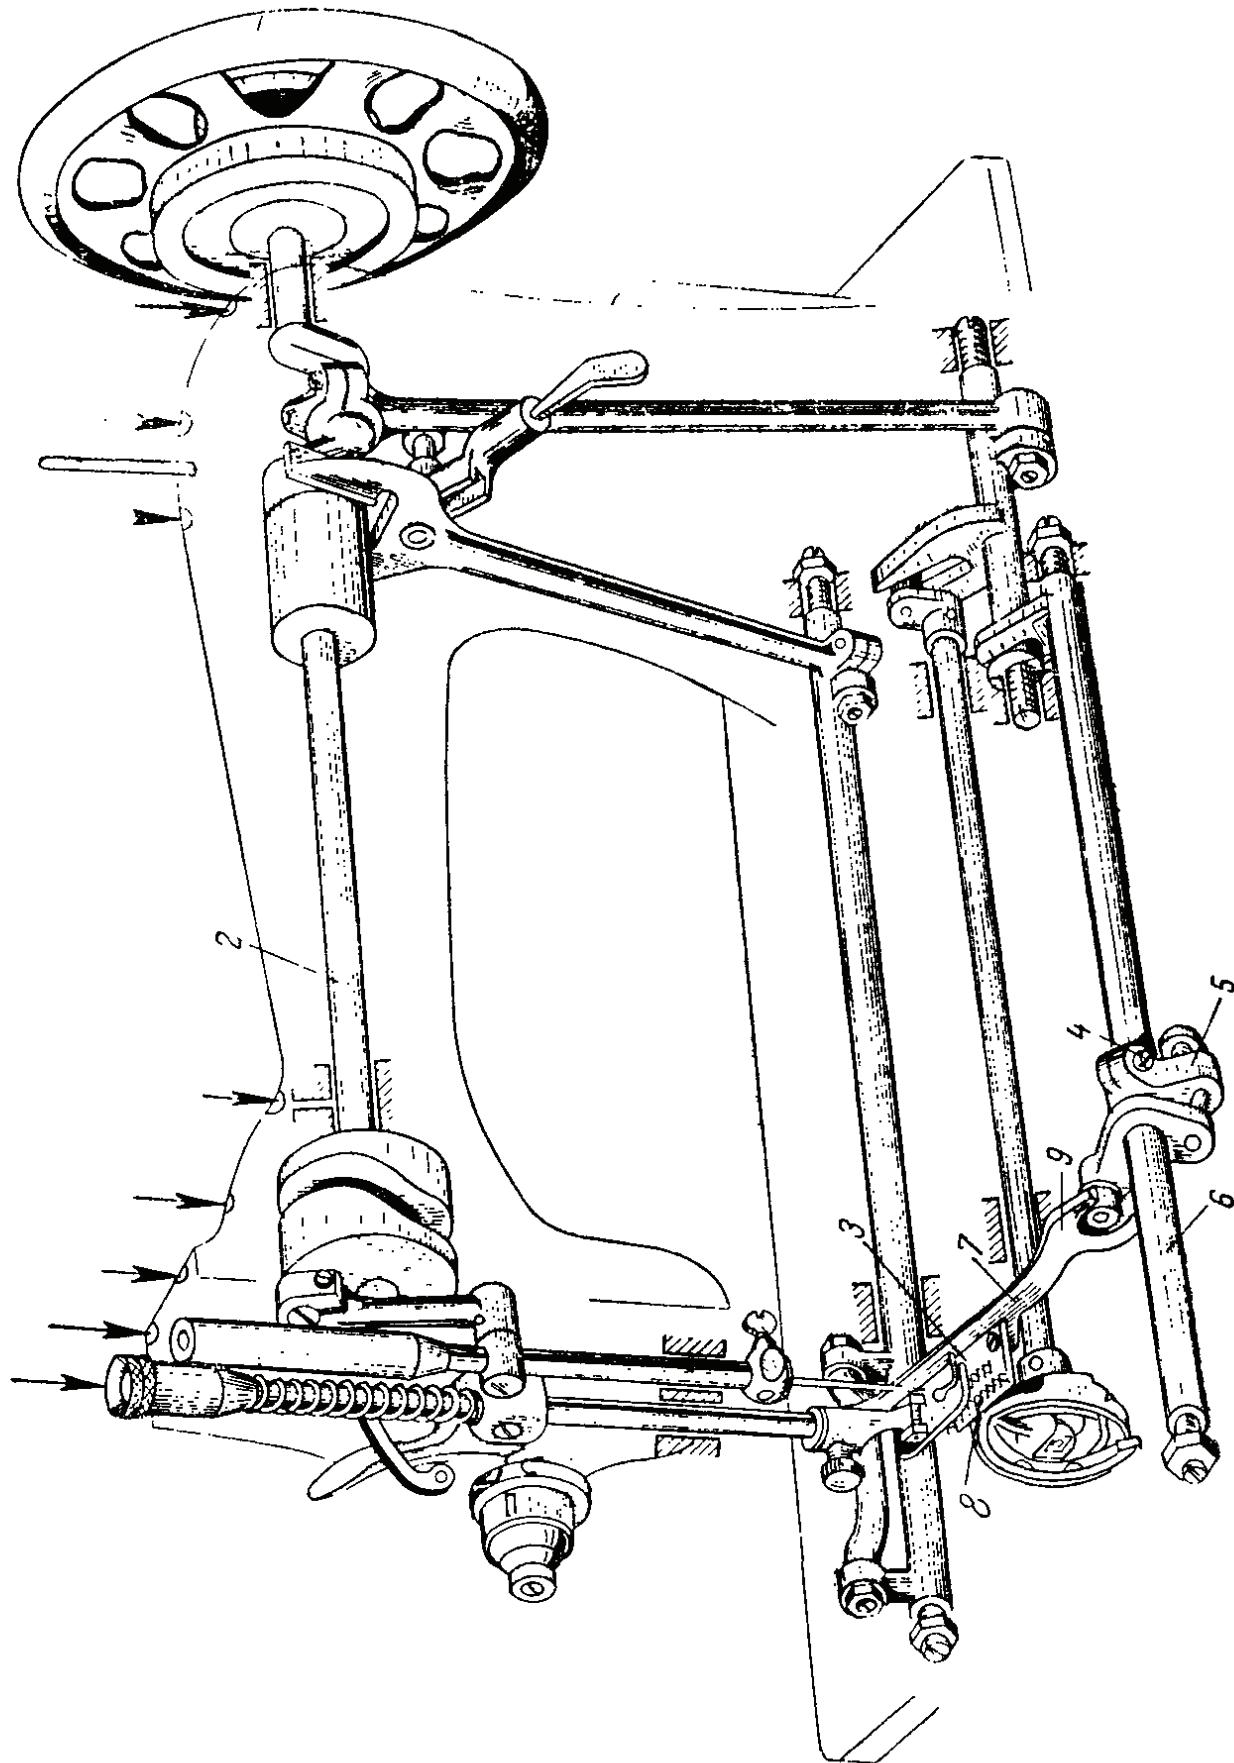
Места смазки деталей машины ПМЗ в рукаре
